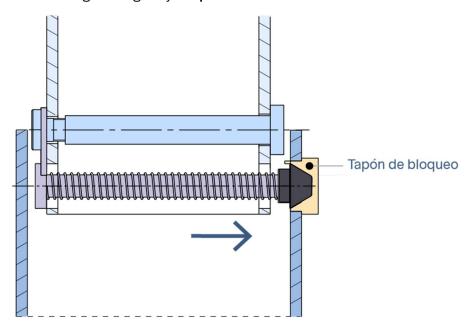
Posición final de bloqueo sistema elevación paneles
